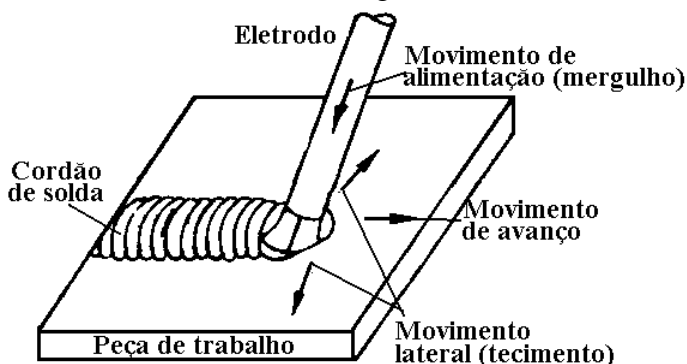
As três movimentações do eletrodo durante a soldagem.
